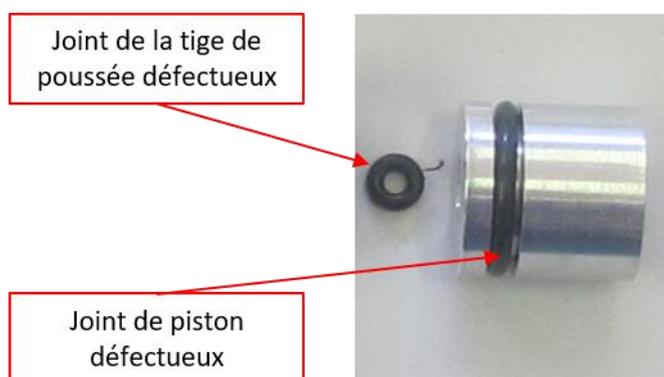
composition interne d'un maître-cylindre, joints défectueux
